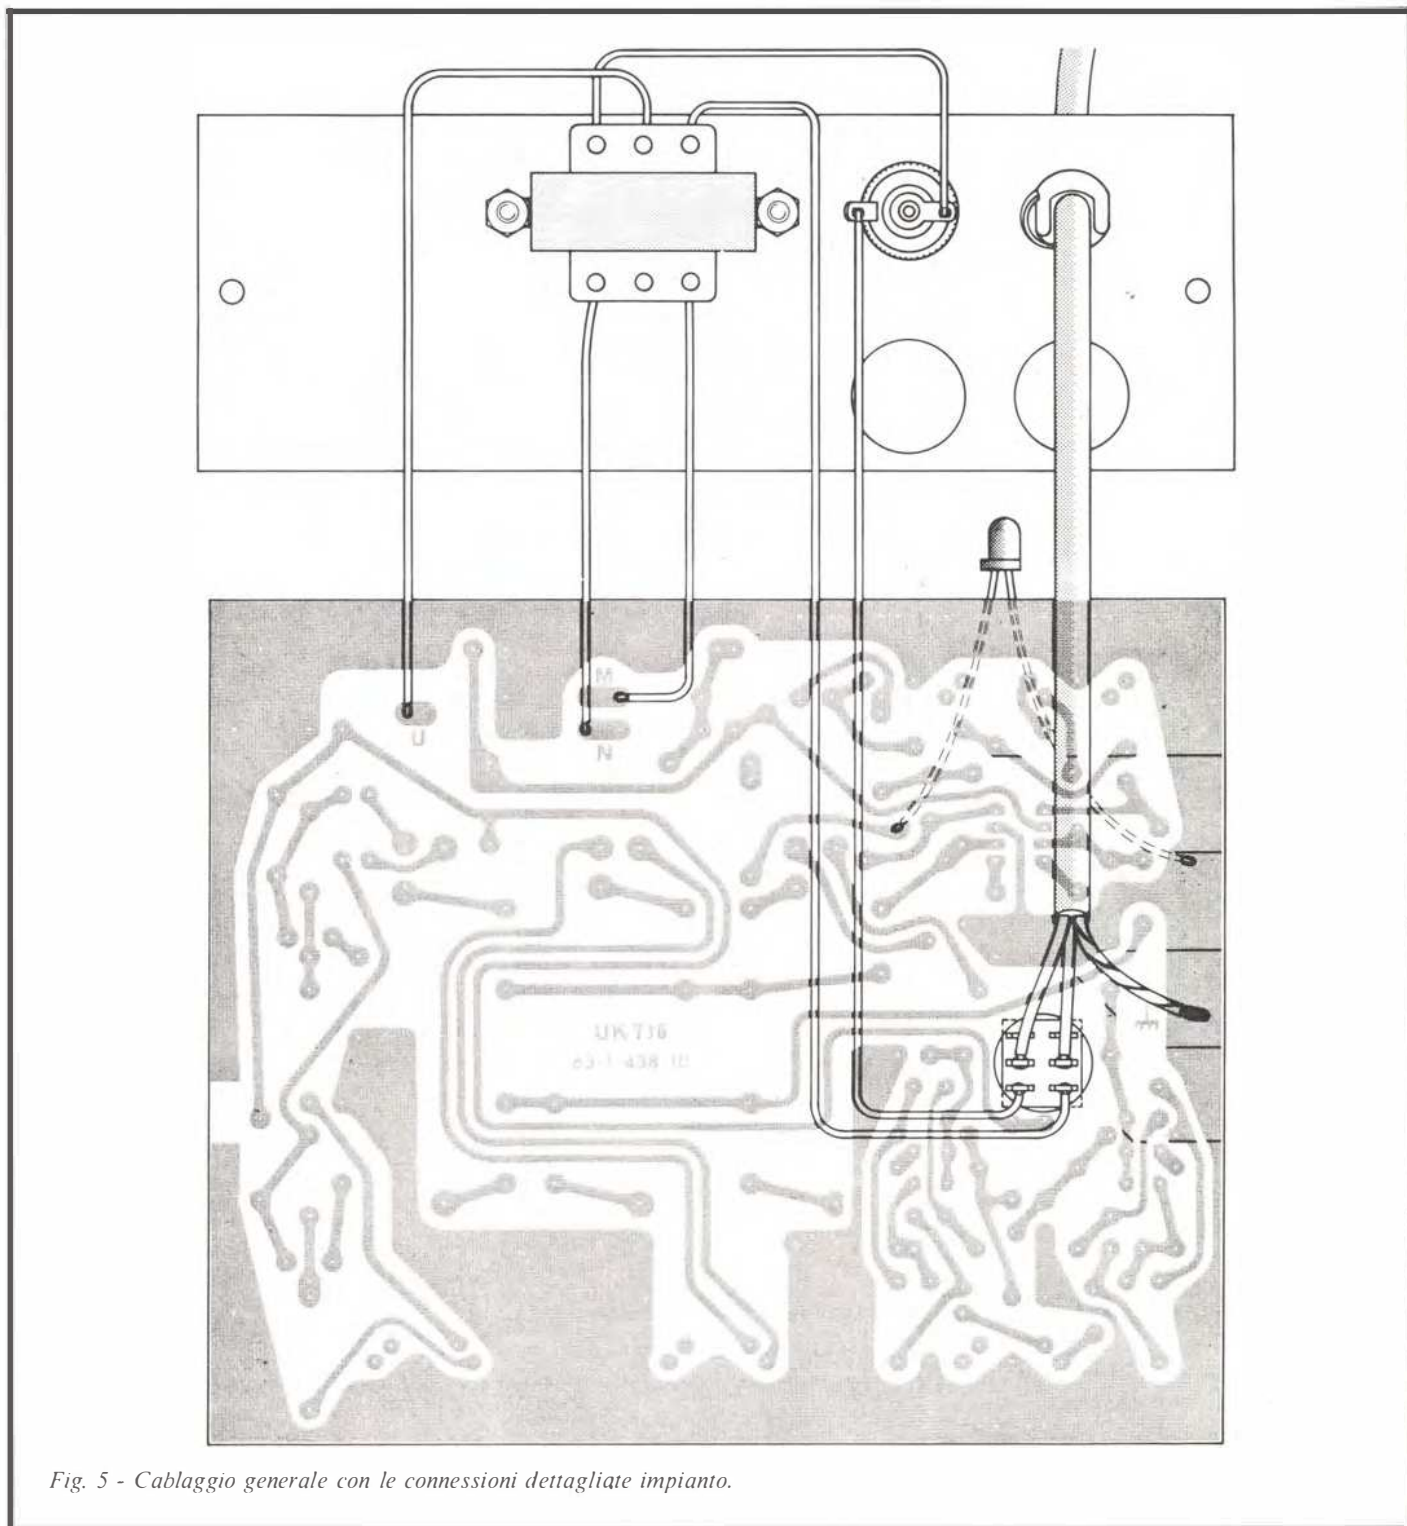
Cablaggio generale con le connessioni dettagliate impianto.
